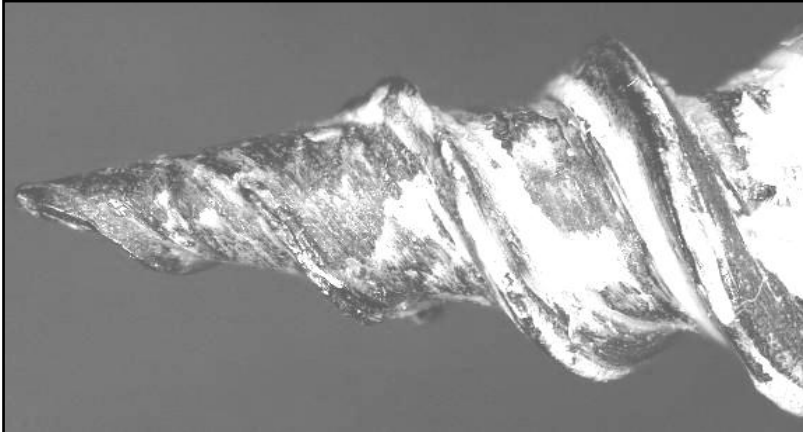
Sichtbarmachung der WF einer Schraube beim Einschraubvorgang durch weiße Farbe – WF sind dort, wo die weiße Farbe abgetragen wurde
